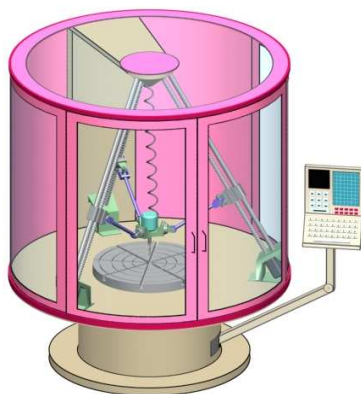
Многокоординатный сверлильно-фрезерный станок повышенной жесткости
